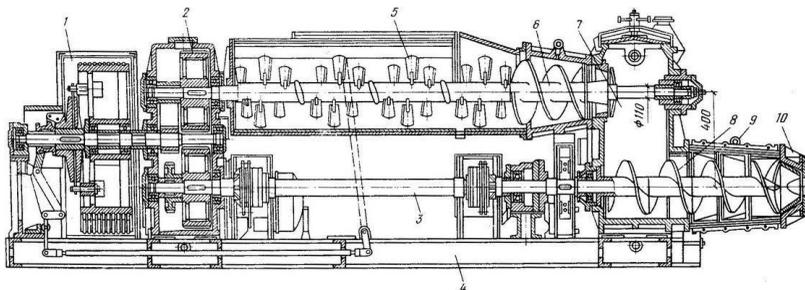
Ленточный комбинированный вакуумный пресс СМ-443А: 1 – коробка привода; 2 – система передач; 3 – вал; 4 – станина; 5 – смеситель; 6 – верхний шнек; 7 – вакуум-камера; 8 – нижний шнек; 9 – цилиндр; 10 – головка прессы
